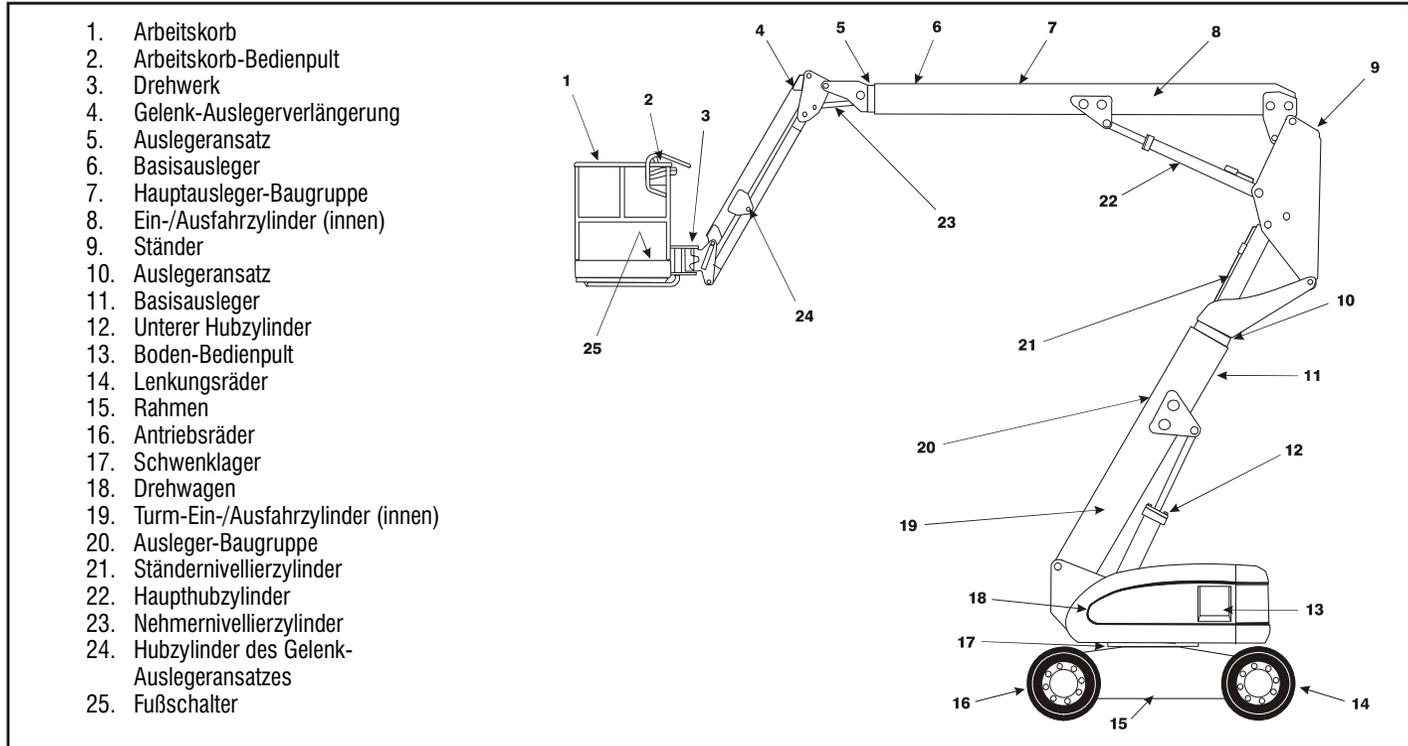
Maschinenbezeichnungen – 600AJ
